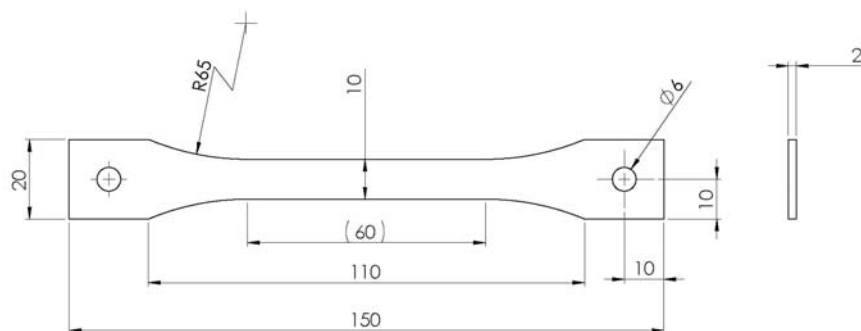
Geometria e dimensões do provete de adesivo utilizado no ensaio de tracção.
